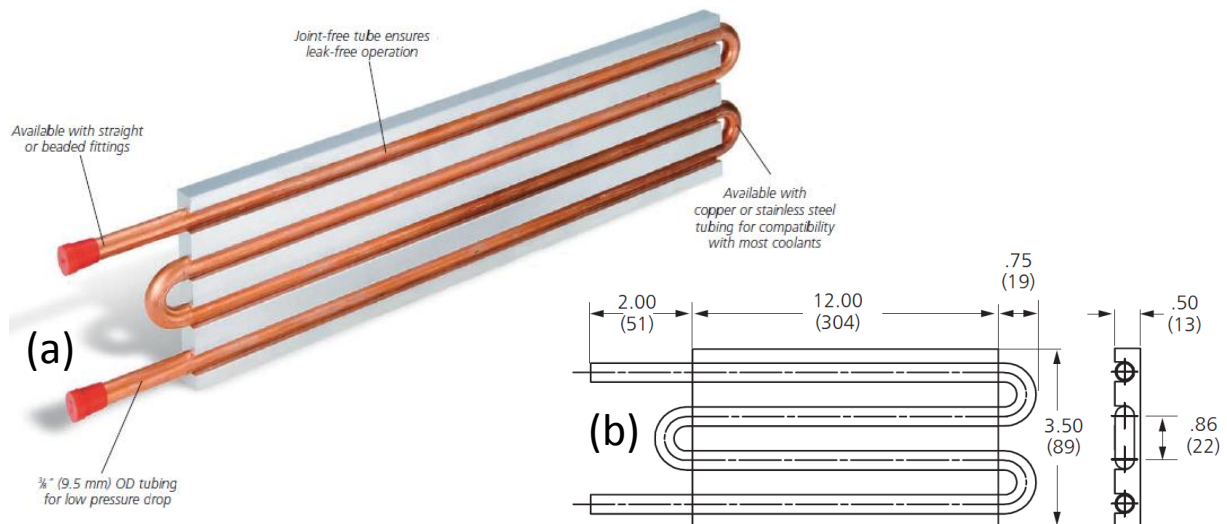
(a) photo de la plaque ; (b) dimensions de la plaque froide en pouce et entre parenthèses en millimètres
